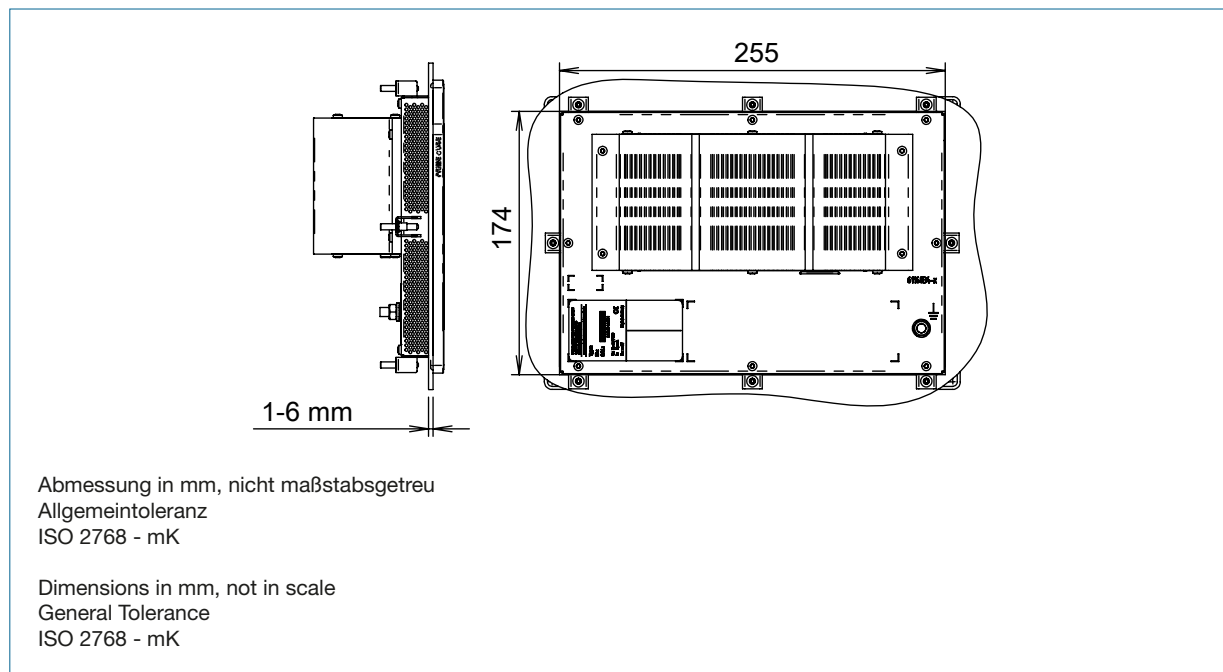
10,1" Prime Panel Pico Einbau - Einbauausschnitt
